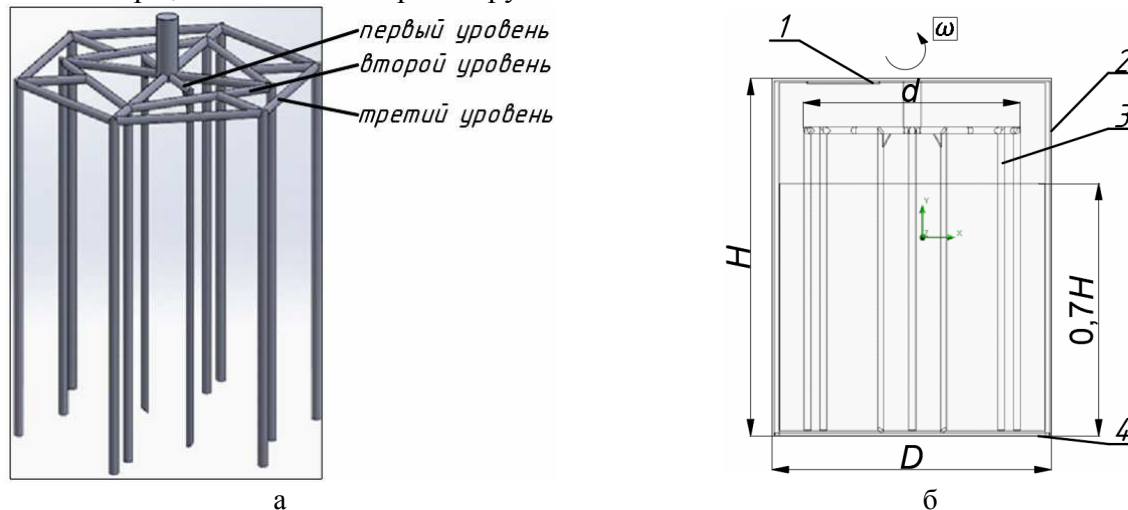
Вертикальный стержневой рабочий орган: а – цифровой двойник рабочего органа; б – расчетная модель смесительно-нагревательного устройства: 1 – загрузочное отверстие; 2 – смесительная камера; 3 – вертикальный стержневой рабочий орган; 4 – шиберный затвор
